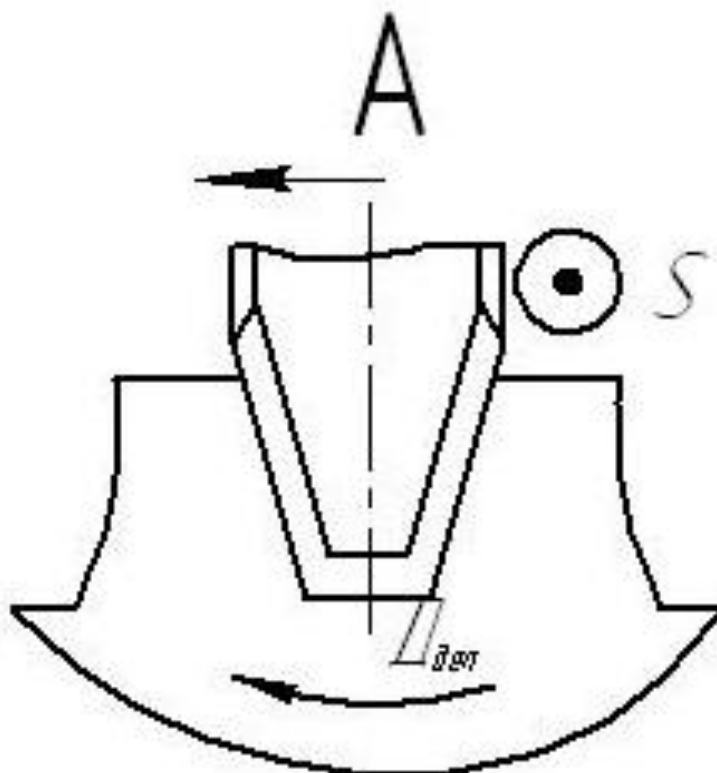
Схема обработки зубьев зубострогальным резцом.
